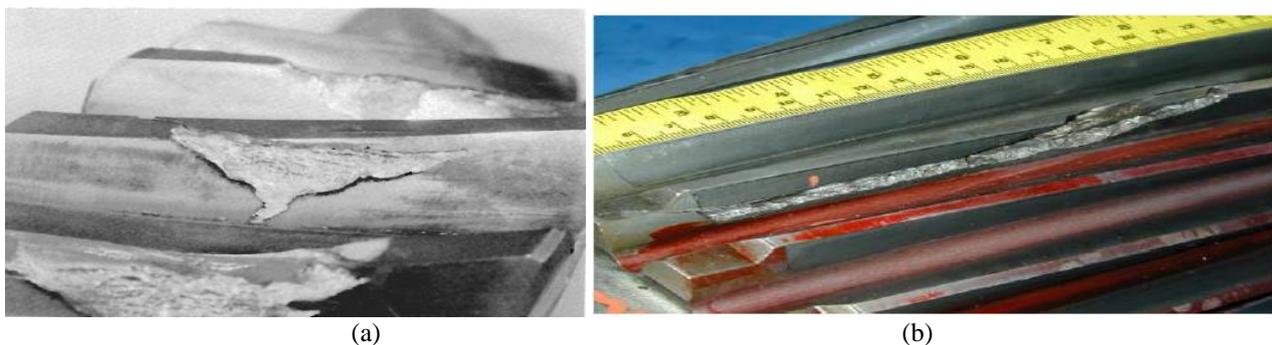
(a) *Scuffing* pada *pinion gear* [6], dan (b) *Fretting corrosion* [6]
